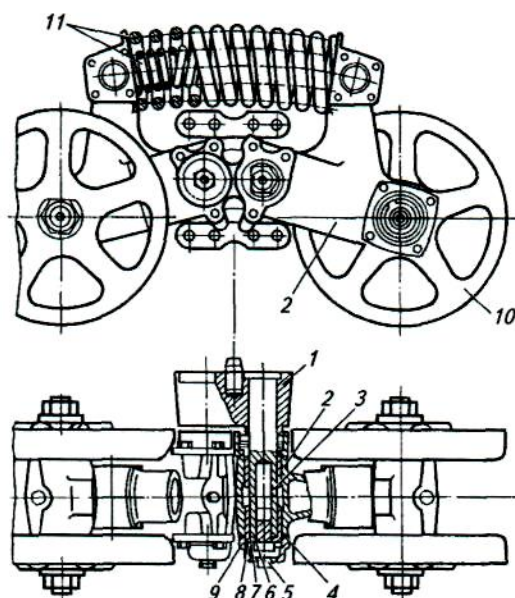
Каретка подвески трактора ХТЗ-150-09
